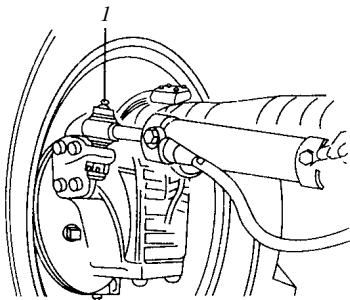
Смазка шарниров гидроцилиндра ГОРУ:
